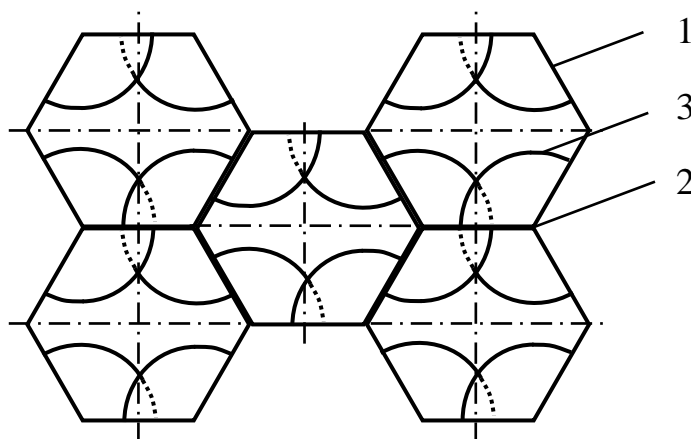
Схема конструктивного исполнения насадки: 1 – пакет насадки; 2 – лист насадки; 3 – перегородки
